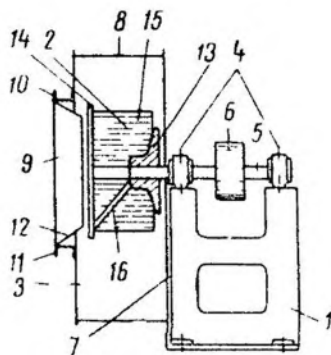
Схема центробежного вентилятора типа „Сирокко“
